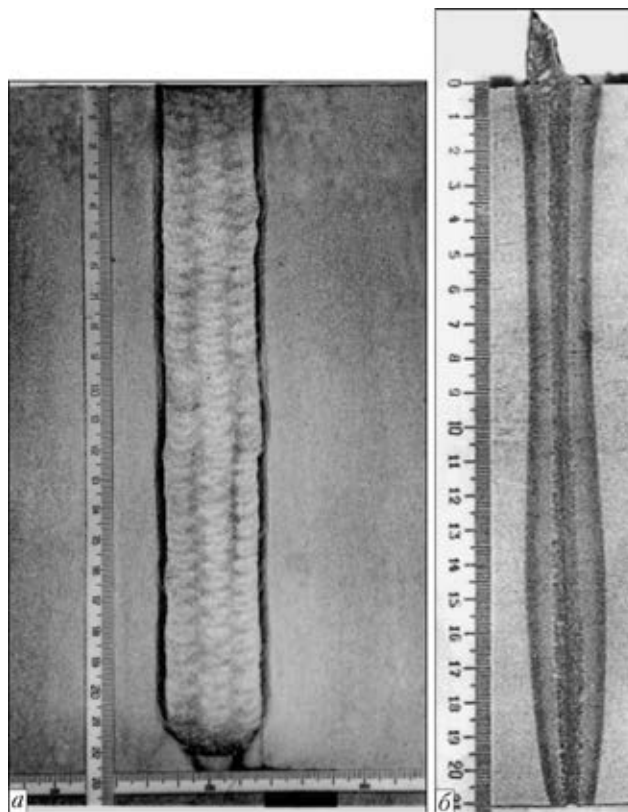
Макрошлифы поперечного сечения кольцевых швов низколегированной стали большой толщины, выполненных многослойной дуговой сваркой под флюсом (а) и однопроходной ЭЛС (б)
